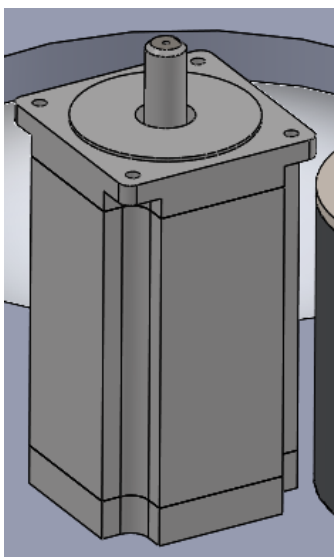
FL86STH шаговый двигатель.
